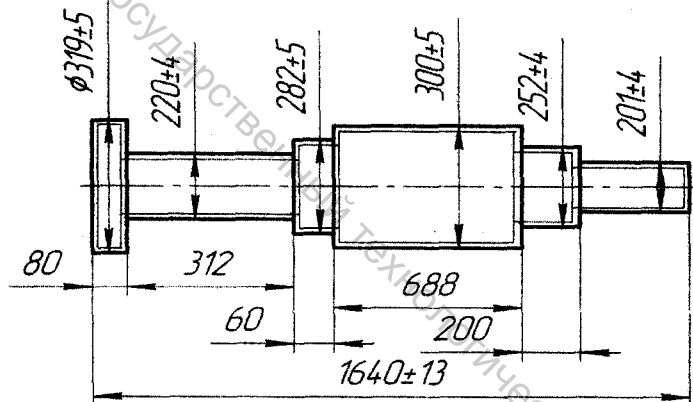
Поковка с основными и дополнительными припусками
